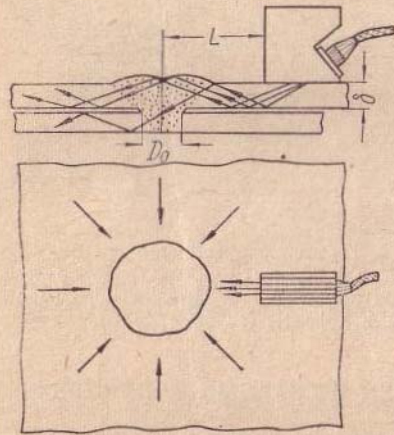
Схема прозвучивания сварной заклепки.
